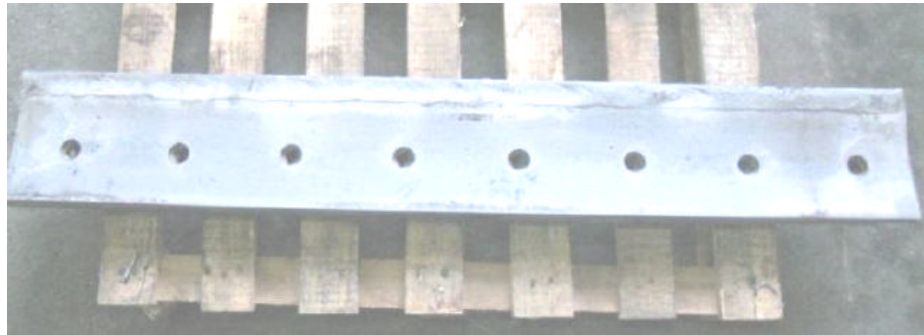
Загальний вигляд ножа бульдозера після наплавлення
